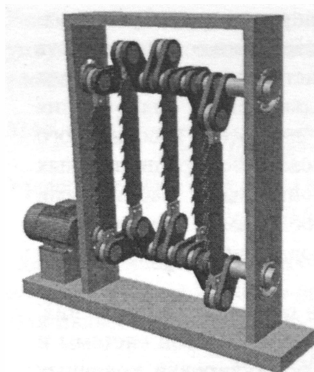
Принципиальная схема «коленчатого» станка и опытный образец «коленчатого» станка "Шершень" M2001
